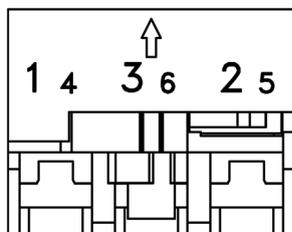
Kennzeichnung der Steckpositionen auf dem 3-fach Halter
